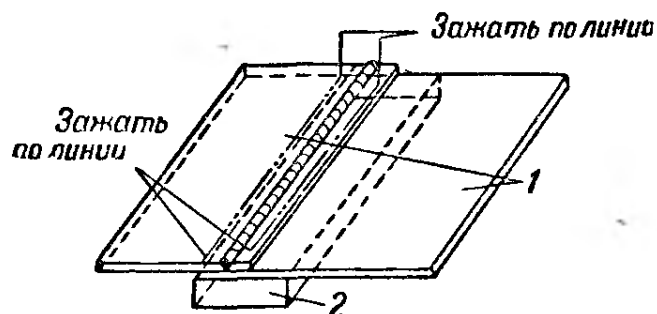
Способ сварки тонких листов стали в нахлестку с проплавлением:
